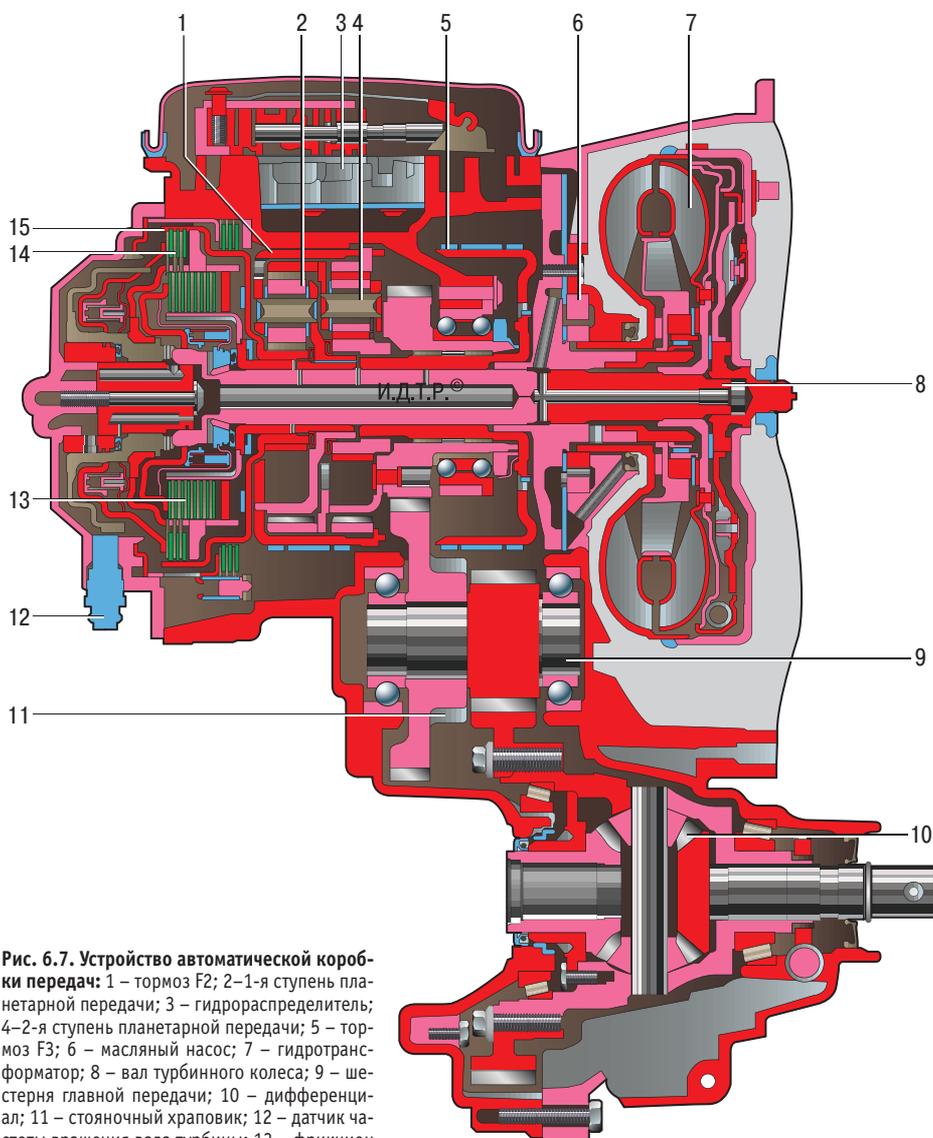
Устройство автоматической коробки передач: 1 – тормоз F2; 2 – 1-я ступень планетарной передачи; 3 – гидрораспределитель; 4 – 2-я ступень планетарной передачи; 5 – тормоз F3; 6 – масляный насос; 7 – гидротрансформатор; 8 – вал турбинного колеса; 9 – шестерня главной передачи; 10 – дифференциал; 11 – стояночный храповик; 12 – датчик частоты вращения вала турбины; 13 – фрикцион E1; 14 – фрикцион E2; 15 – тормоз F1
